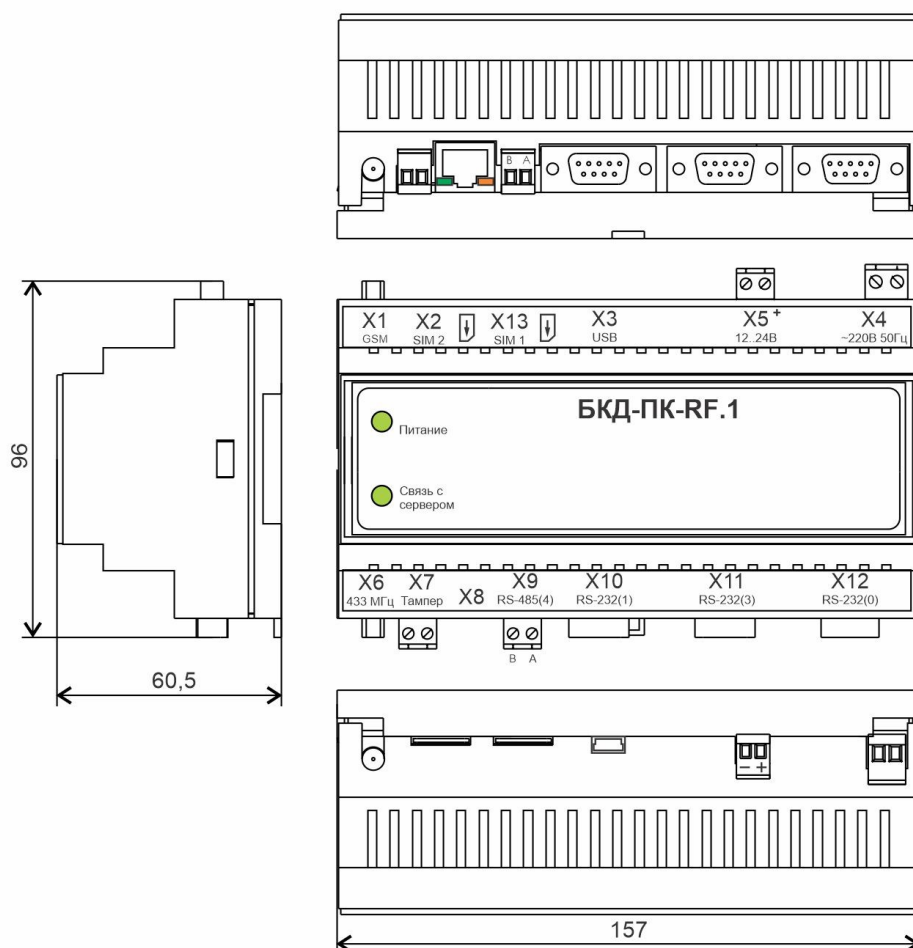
Габаритные размеры БКД-ПК-RF.1
